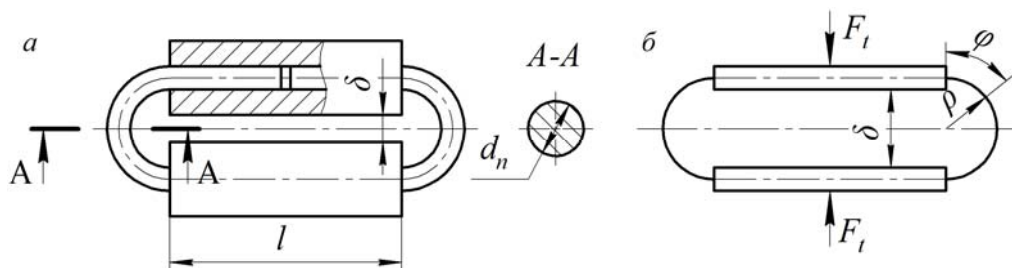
Схема установки підковоподібних пружин: а – конструктивна; б – розрахункова
